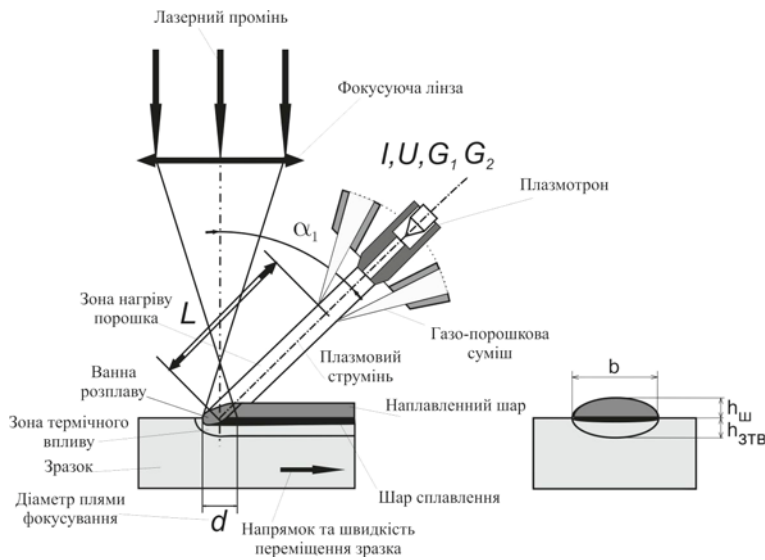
Схема процесу лазерно-плазмового газопорошкового наплавлення
